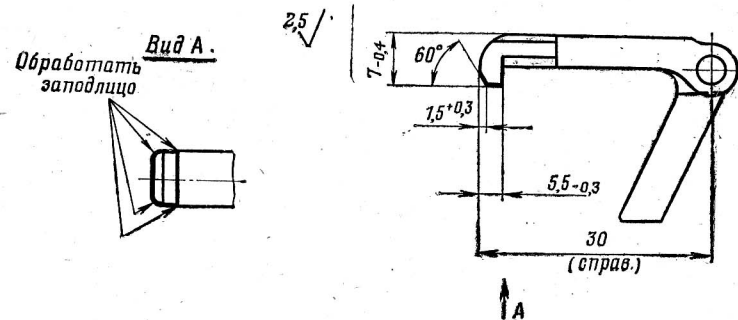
Обработка зуба зацепа пулемета РПКС74 после наплавки
